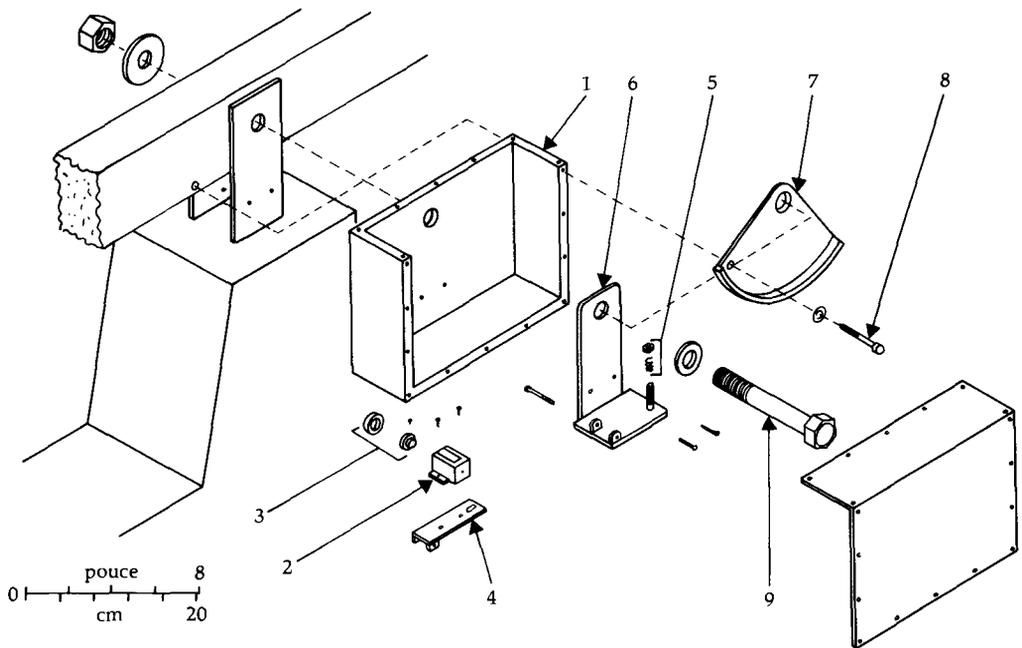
Modèle de support du compteur mécanique : 1) carter ; 2) compteur ; 3) roue et rondelle de caoutchouc du compteur ; 4) support du compteur ; 5) écrou de réglage et ressort du compteur ; 6) assemblage du guide ; 7) balancier ; 8) goupille de balancier ; et 9) boulon du bras de pompe.
